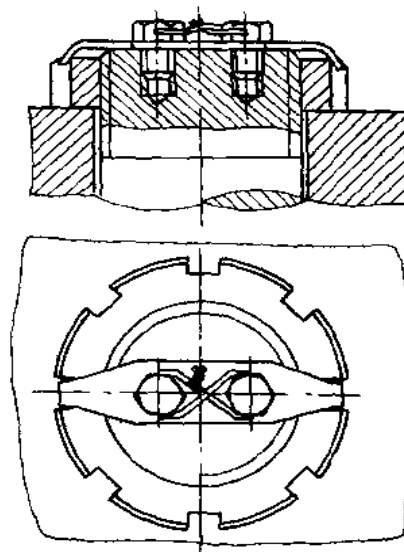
用两个螺钉连锁固定 U 形挡板
